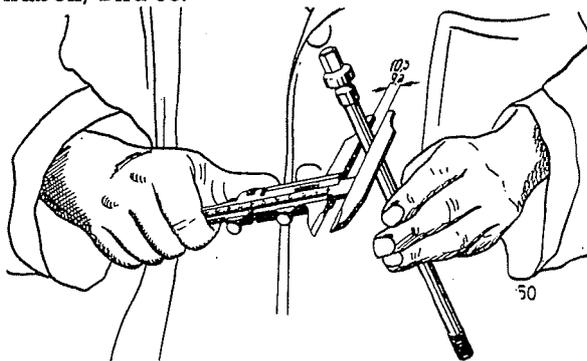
Schaftdurchmesser der Zylinderkopfschraube
